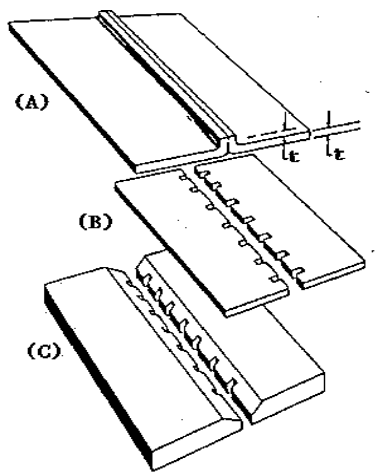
Preparação das bordas para a soldagem de alumínio.
